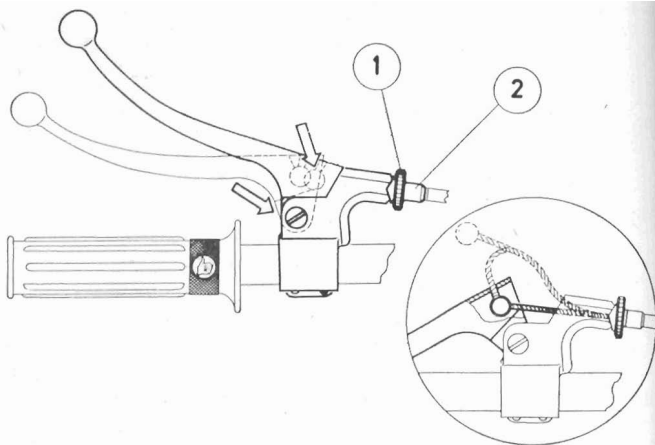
Mando embrague: Reglaje, engrase y cambio de cable.
